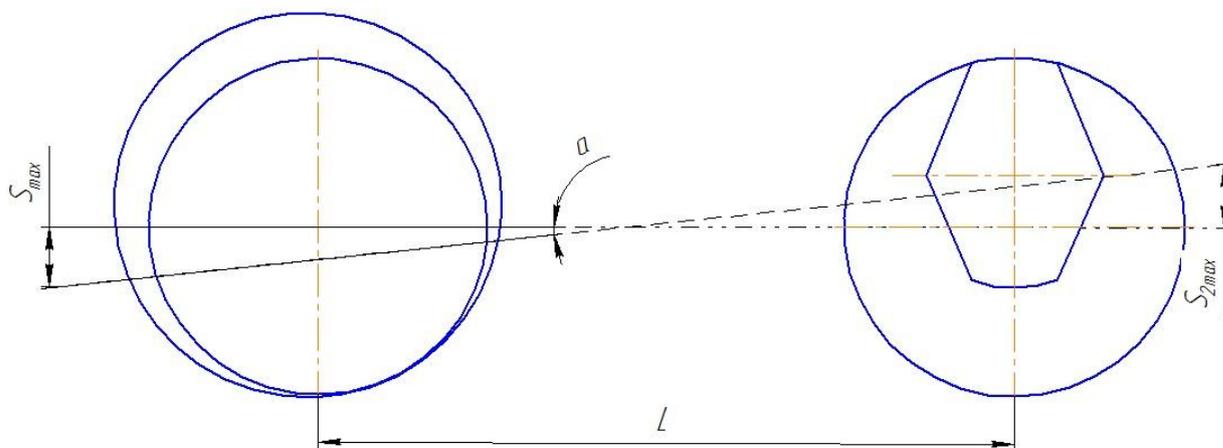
Схема перекоса заготовки, установленной на два пальца
